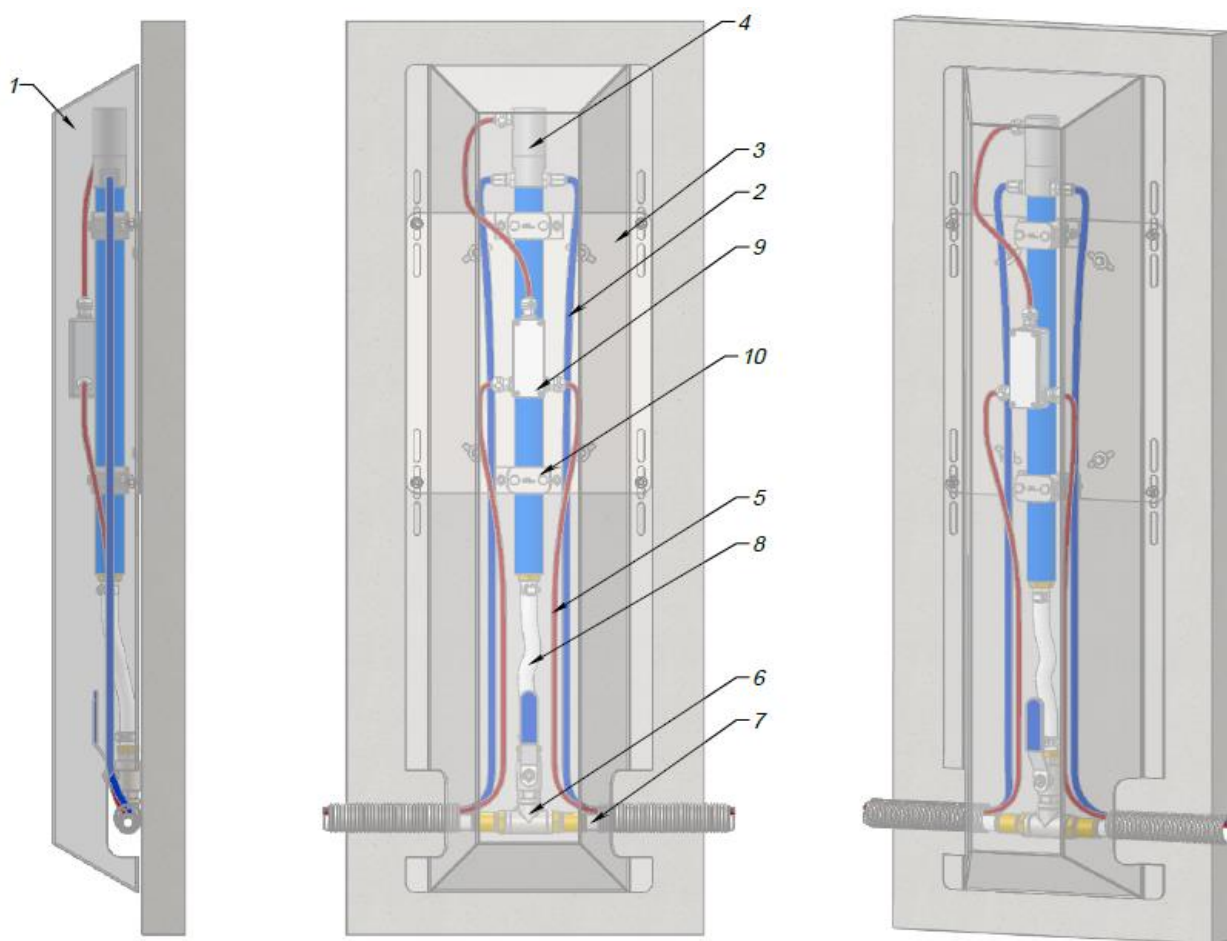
Внешний вид преобразователя уровня с защитным кожухом
